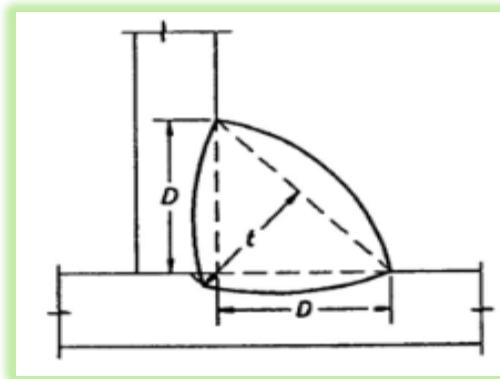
Soldadura de filete (Kobelco, 2022)
